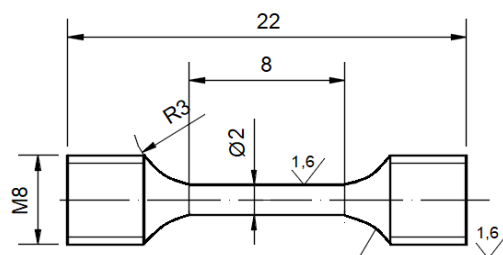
Форма вспомогательного образца для испытаний:
